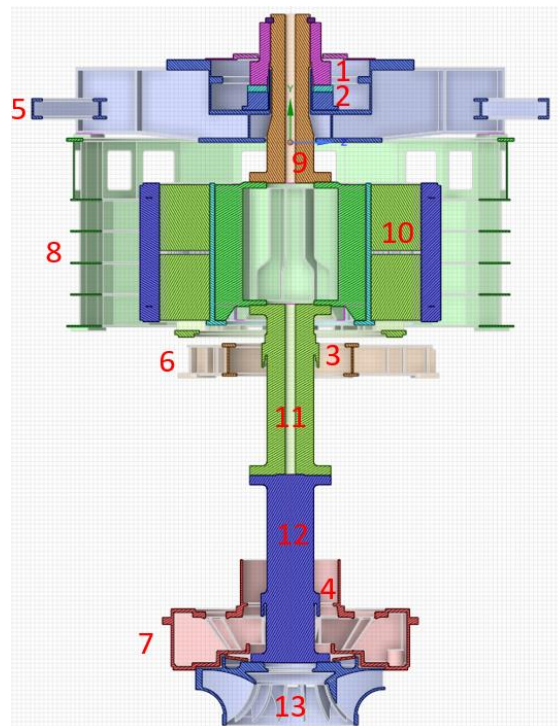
Partes principales del conjunto generador-eje-turbina
